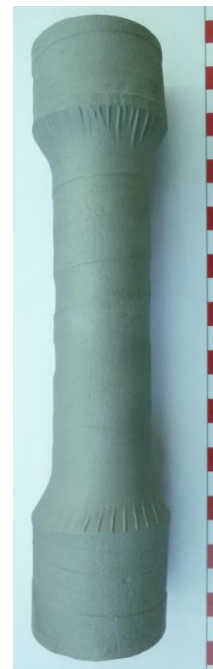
Vue de la préforme haltère laminée à un taux de réduction de 35%, diamètre initial 50mm [THESE/IWU]
